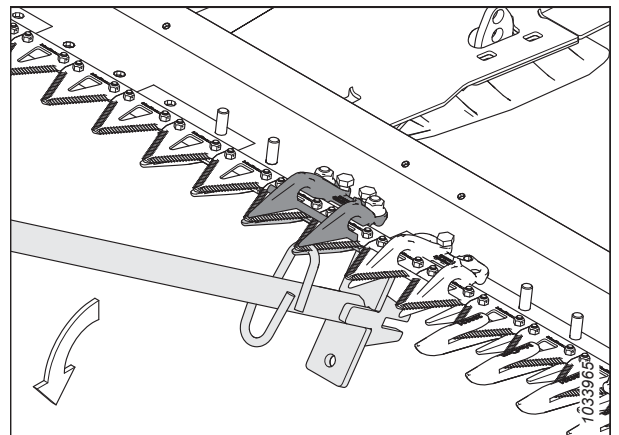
Регулировка смещением вниз — укороченный противорежущий палец
